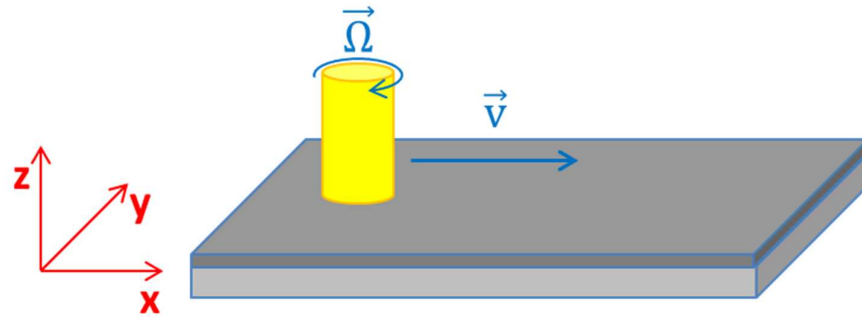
Configuration de soudage à l'échelle du laboratoire.
